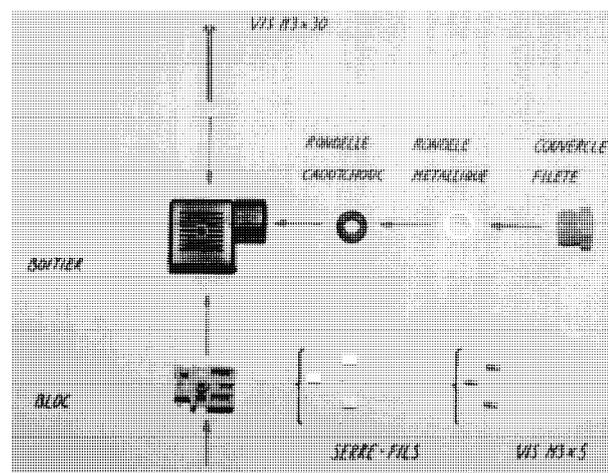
Exemple de produit qu'il faut assembler
